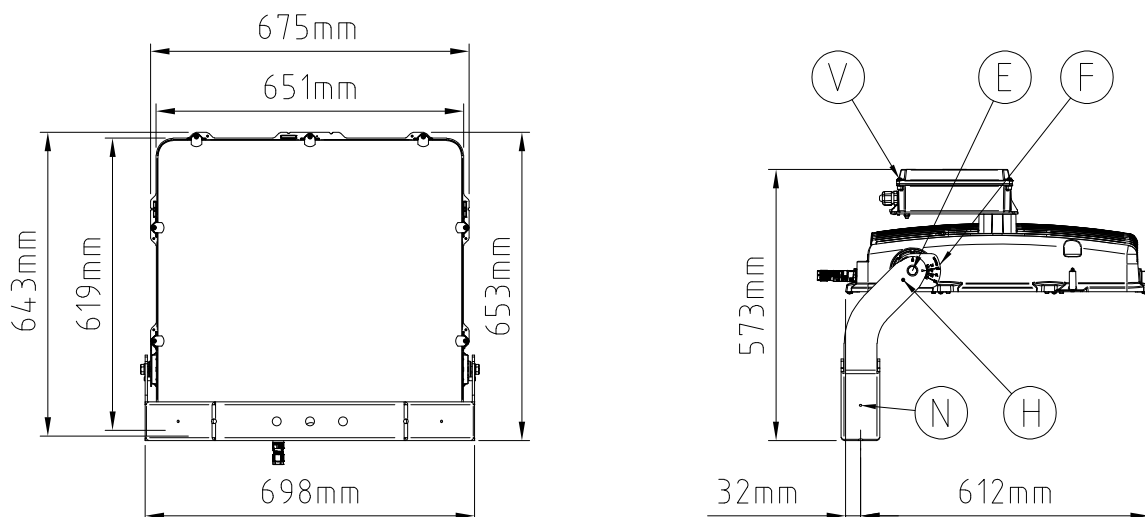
LEDMASTER ONE - Driver remoto | Remote driver
